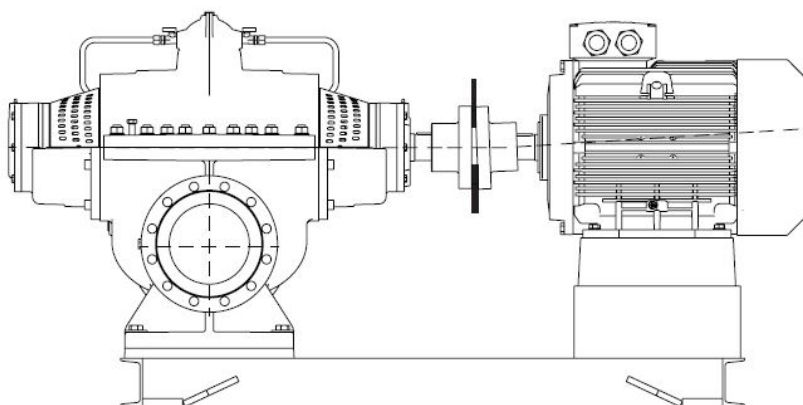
Erreur angulaire dans le plan horizontal
